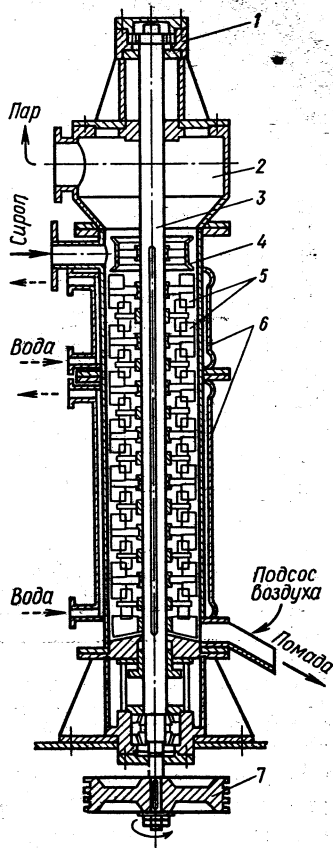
Схема вертикального пленочного аппарата-кристаллизатора роторного типа для приготовления помады:
